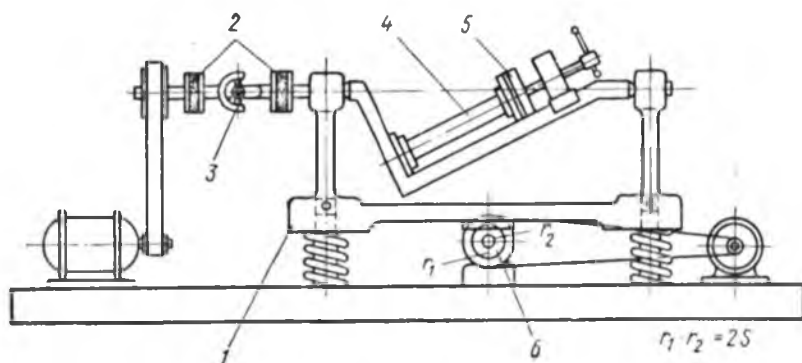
Схема устройства для полирования токонесущих поверхностей стальными шариками:
